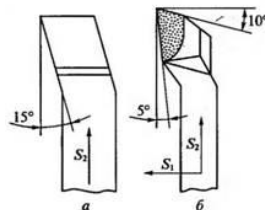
Подрезной резец: а – из быстрорежущей стали; б – армированный пластинкой твердого сплава; S_1 и S_2 – подача
